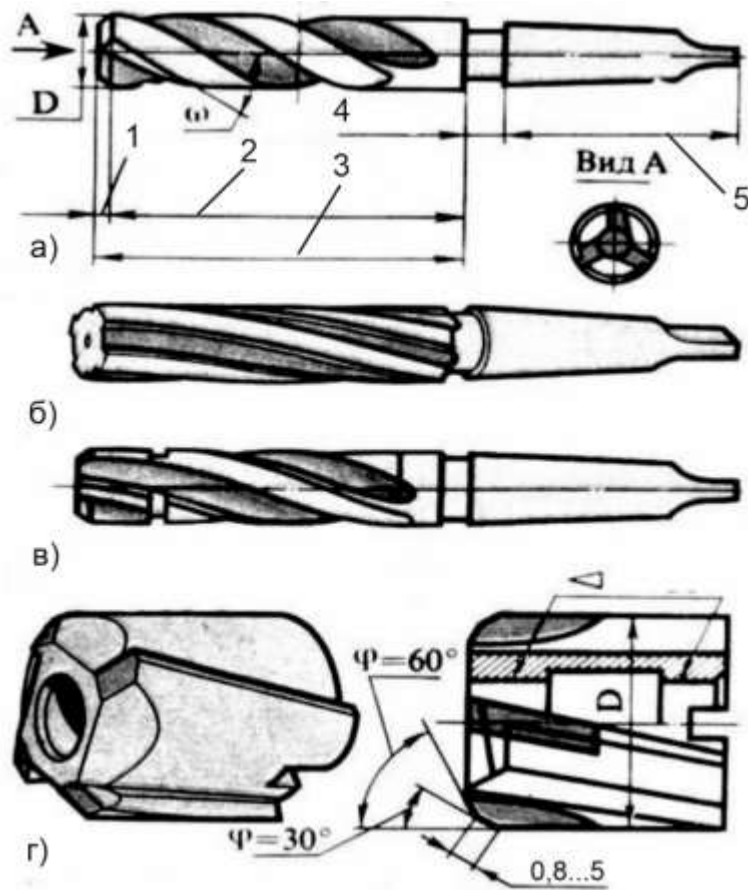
Конструкція та виконання цілісних та насадних зенкерів: 1 – ріжуча частина; 2 - калібруюча частина; 3 – робоча частина; 4 – шийка; 5 – хвостовик.
